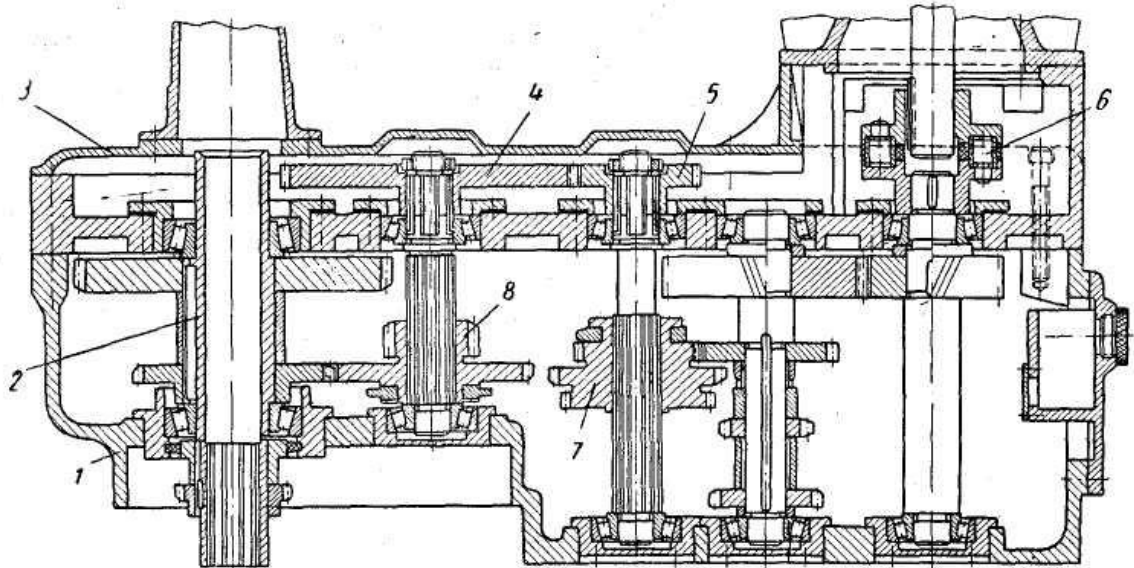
Конструкція приводу головного руху вертикально-свердлувального верстата
